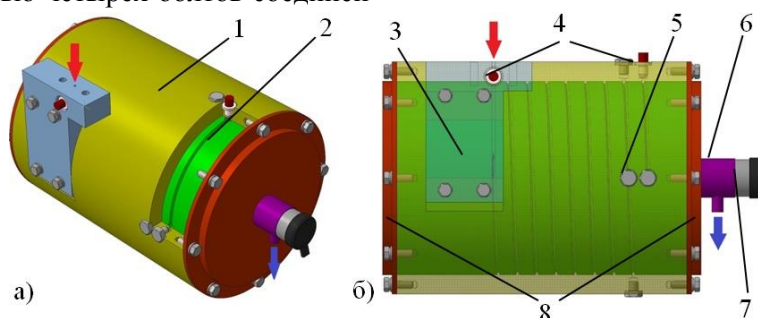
Устройство для снятия характеристики впрыскивания: 1 – корпус, 2 – внутренняя обойма, 3 – приемный штуцер, 4 – тензометрические датчики давления, 5 – заглушки, 6 – сливной штуцер, 7 – клапанный регулятор давления, 8 – крышки.
